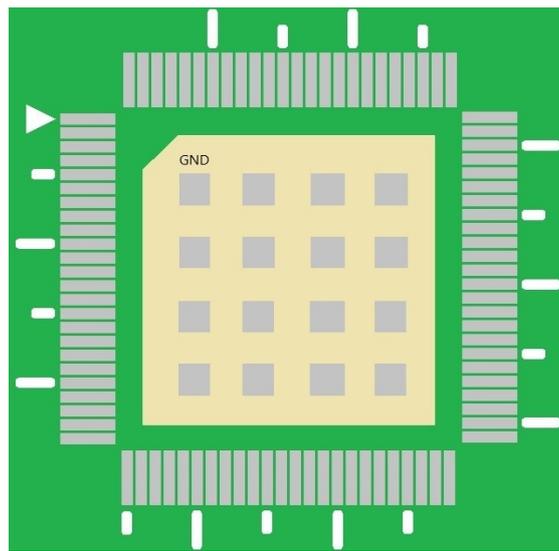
LT7589A 底部焊盘 PCB 的设计建议-1
